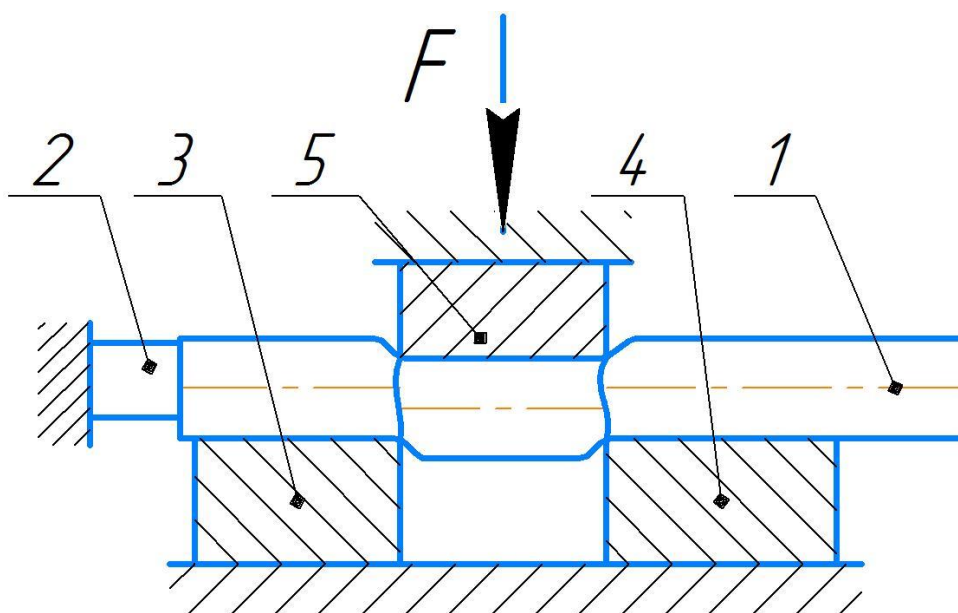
Принципова схема штампа, в якому реалізована двохопорна схема відрізки зсувом [13]
